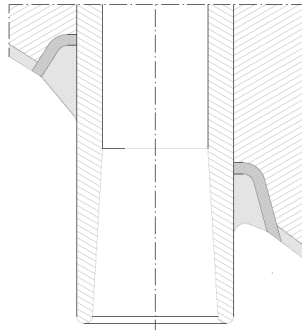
Conception actuelle des soudures des adaptateurs du couvercle
